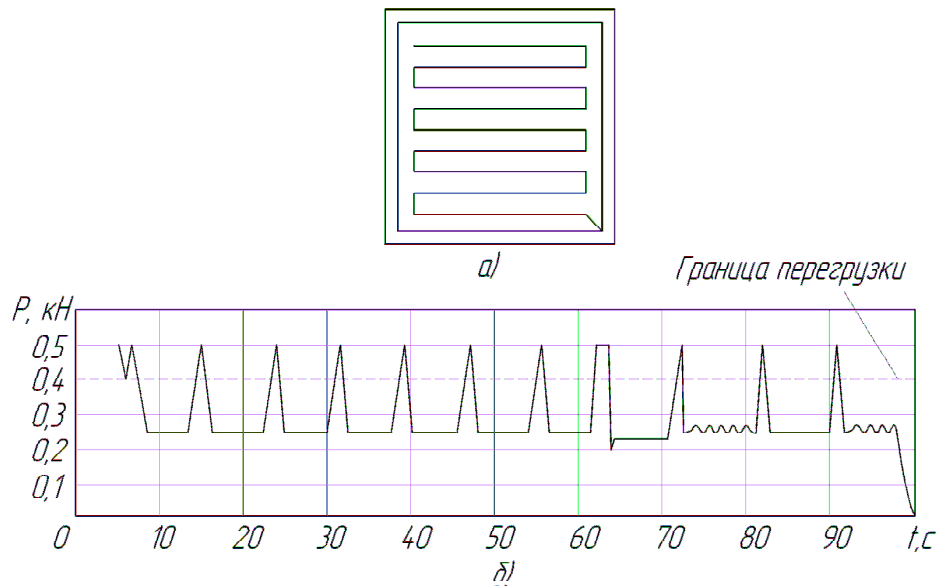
Фрезерование квадратного кармана зигзагом:
